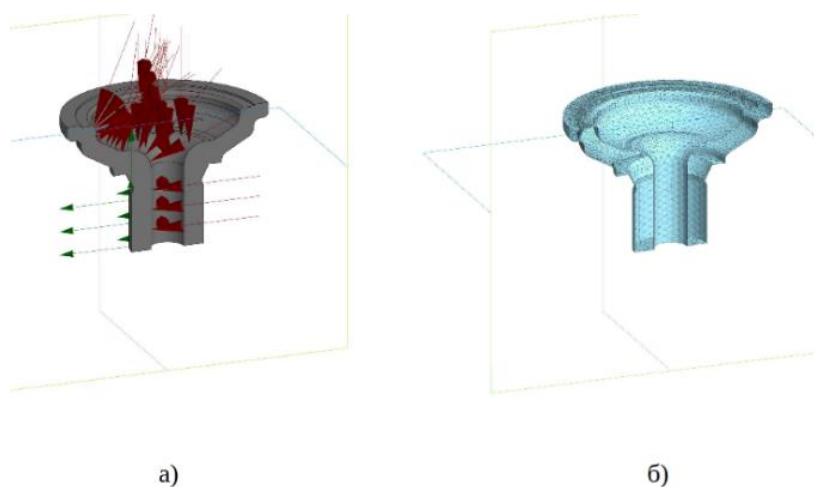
Корпус а) схема расстановки нагрузки и закрепления; б) сетка конечных элементов
